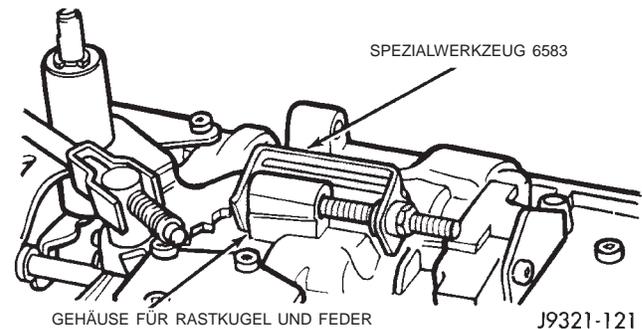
Rastkugel mit Feder mit Haltewerkzeug fixieren
